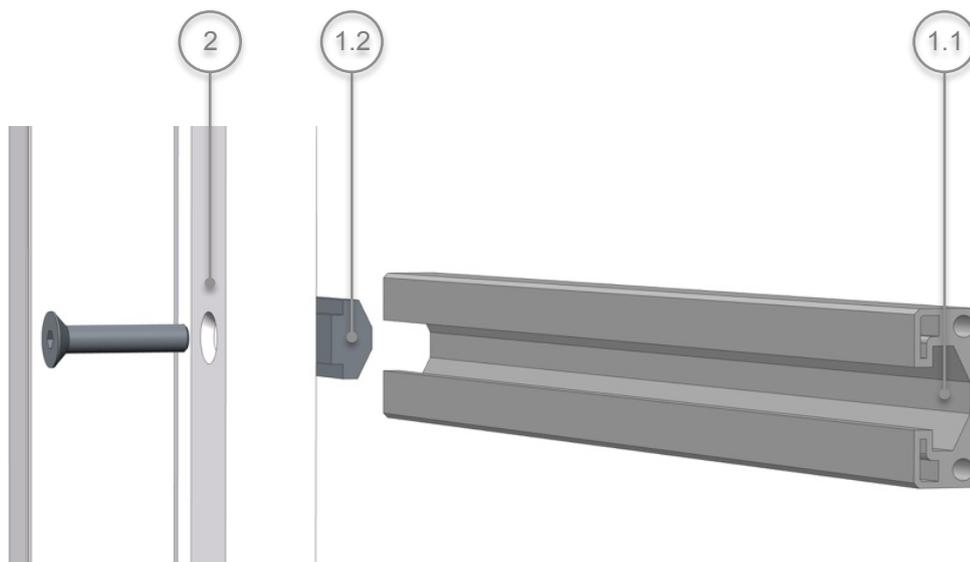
Profilschiene: Befestigung mittels T-Mutter
